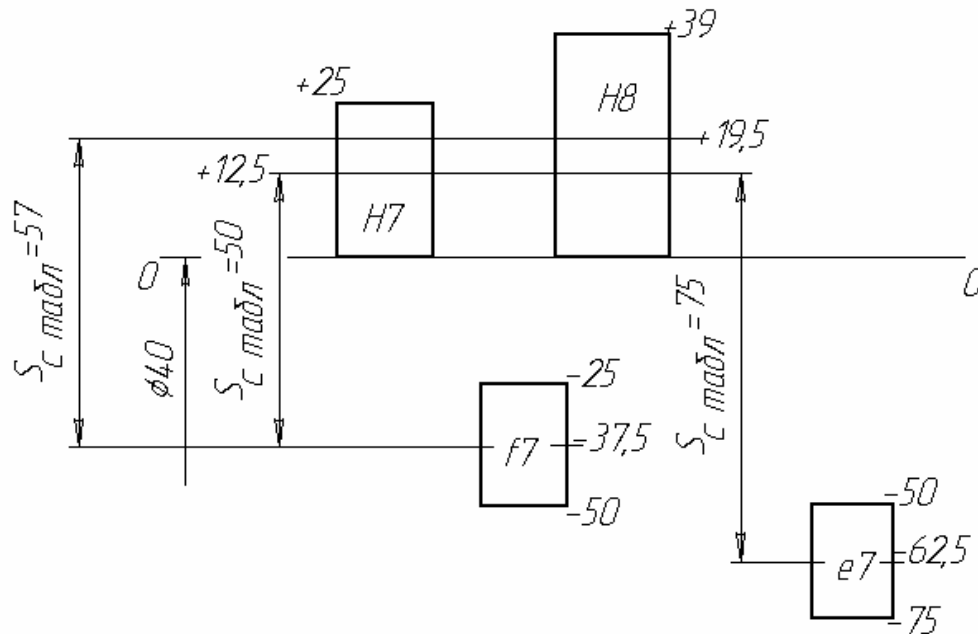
Схема расположения полей допусков вала и подшипника для посадок в системе отверстия
